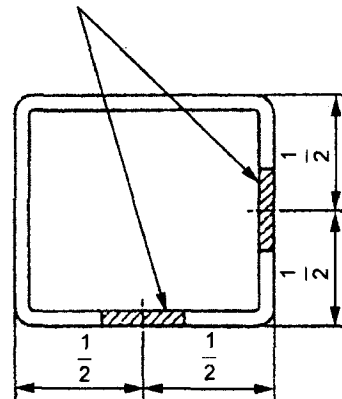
Квадратний і прямокутний поперечний переріз
